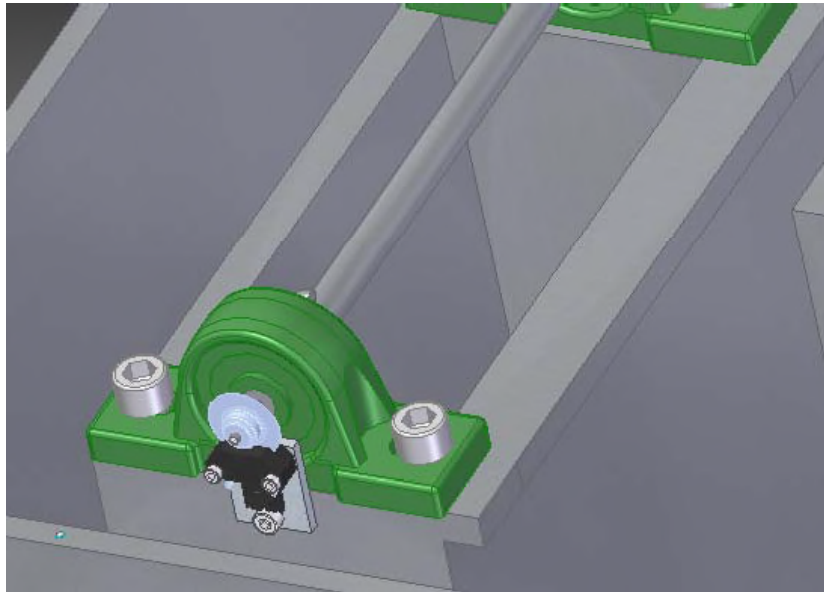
Detalle del montaje del encoder. Fuente: Elaboración propia
